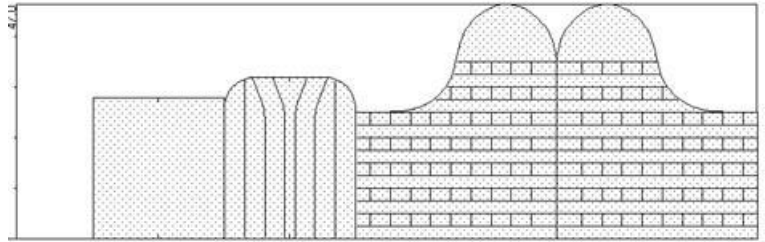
Схема розкладки лекал розвантажувального жилету
